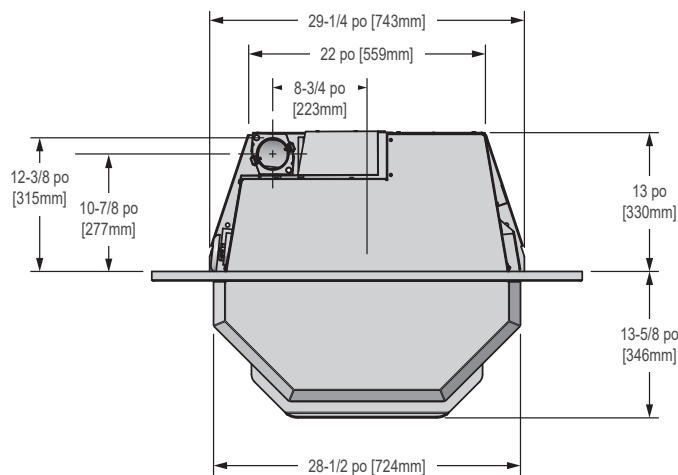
Vue latérale avec jeu de petits panneaux (SP-CB12I3040-NB ou NL)
